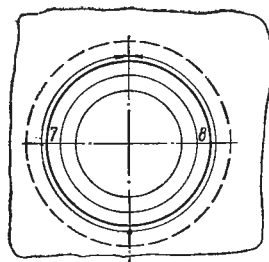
Последовательность приварки лазов к корпусу резервуара и колокола (обозначена цифрами):
